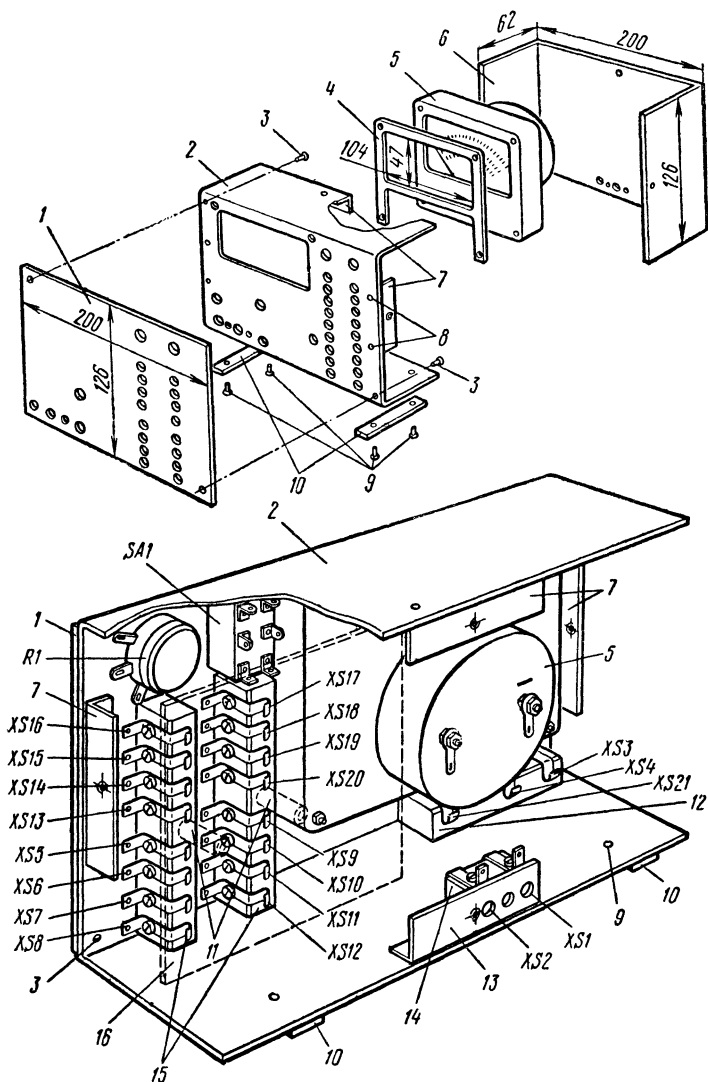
Конструкция корпуса и размещение в нем деталей авометра:
